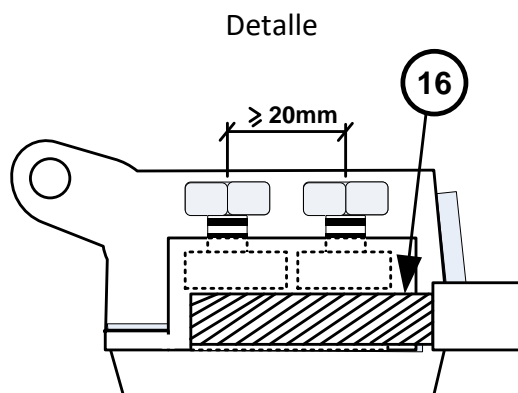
c. Diseño de la bornera con doble tornillo, una vez montado.
